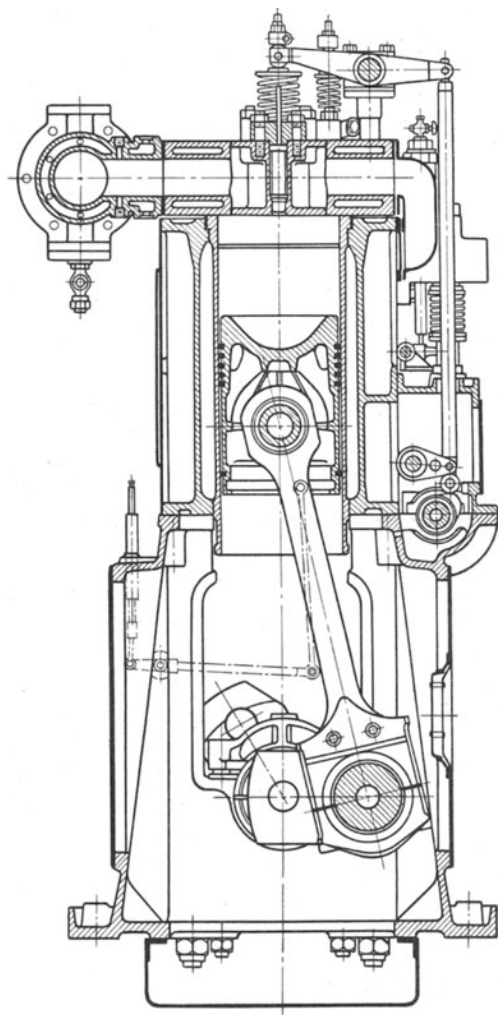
Schnitt durch einen kompressorlosen MAN-Motor.
